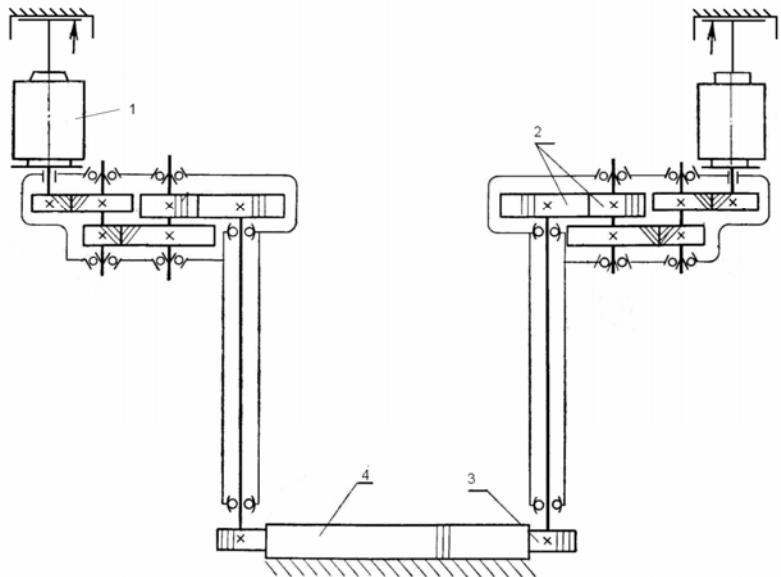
Кинематическая схема двух двигателевого привода механизма поворота драглайна ЭШ 10/70 АО «НКМЗ»: 1 - электродвигатель постоянного тока; 2 - редуктор базовой конструкции привода; 3 - бегунковые шестерни; 4 - зубчатый венец
